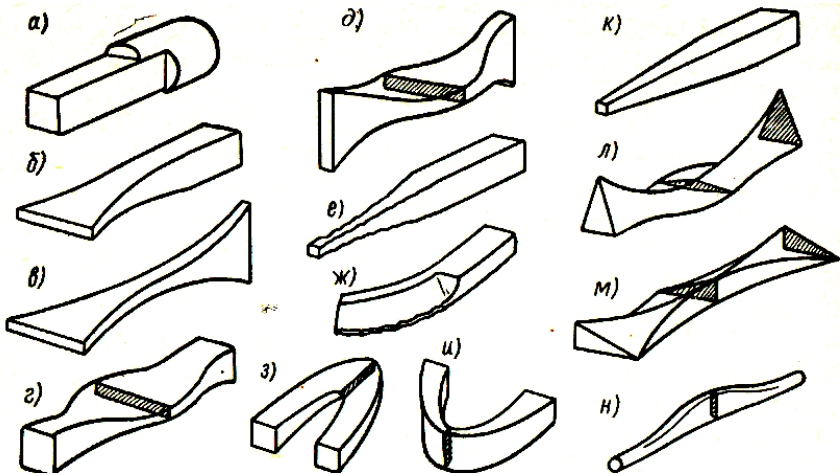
Основные формы заготовок, получаемых методомковки: а - проковка круглой заготовки на квадрат; б - клиновидное уширение штабика; в - заготовка в форме винта; г - заготовка с расплюсченной средней частью; д - клинообразные концы с расширенной серединой; е - заготовка с утонением одного конца; ж - получение заготовки треугольного профиля; з - дугообразная разностенная заготовка; и - то же с разной толщиной вершины дуги; к - заготовка с заостренным концом; л - заготовка треугольного профиля с переменными по длине сечениями; м - кованая заготовка сложной формы; н - круглая заготовка, прокованная на плоскость посередине [6]
